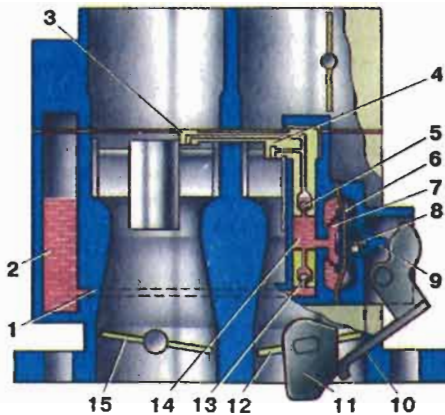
Схема ускорительного насоса карбюратора ДААЗ-2108: 1 – топливный канал; 2 – поплавковая камера; 3, 4 – распылители вторичной и первичной камер; 5 – обратный клапан; 6 – диафрагма; 7 – пружина диафрагмы; 8 – демпфирующая пружина; 9 – толкатель; 10 – рычаг привода; 11 – кулачок привода; 12 – дроссельная заслонка первичной камеры; 13 – всасывающий клапан; 14 – нагнетательный канал; 15 – дроссельная заслонка вторичной камеры
